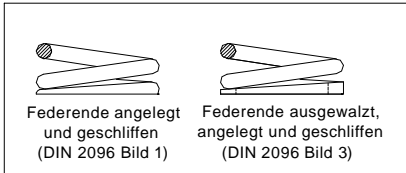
Endenausführungen von Schraubenfedern für Schienenfahrzeuge
